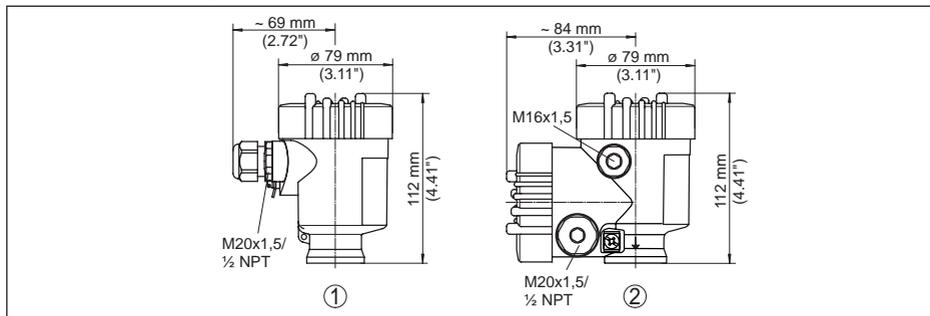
Корпуса в исполнении IP 66/IP 67 (с установленным модулем индикации и настройки корпус выше на 9 мм/0.35 in)
